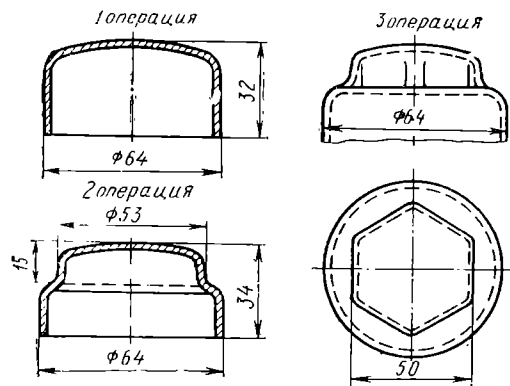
Формоизменяющие операции при штамповке крышки ступицы переднего колеса автомобиля
